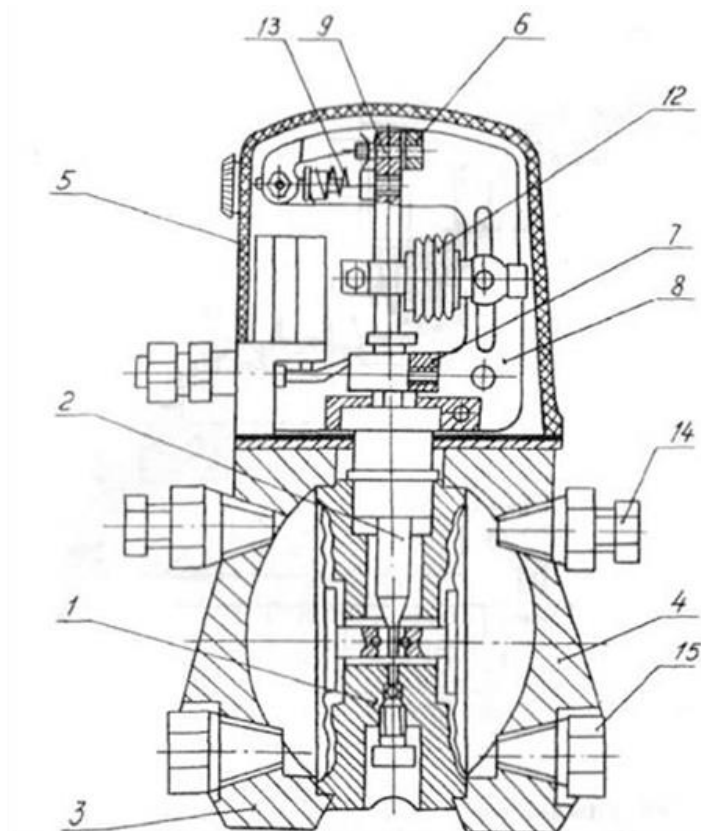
Измерительный преобразователь разности давления 13ДД11 Конструкция
